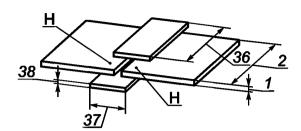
Сборка под шовную контактную стыковую сварку по фольге
